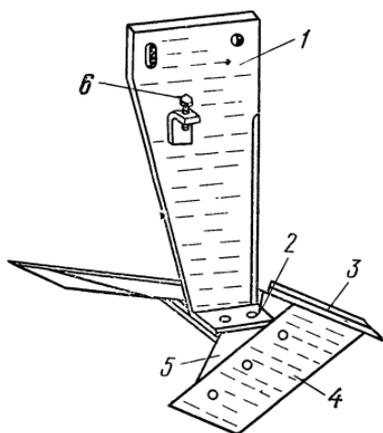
Рабочий орган для глубокого рыхления (ширина захвата 110 см):
